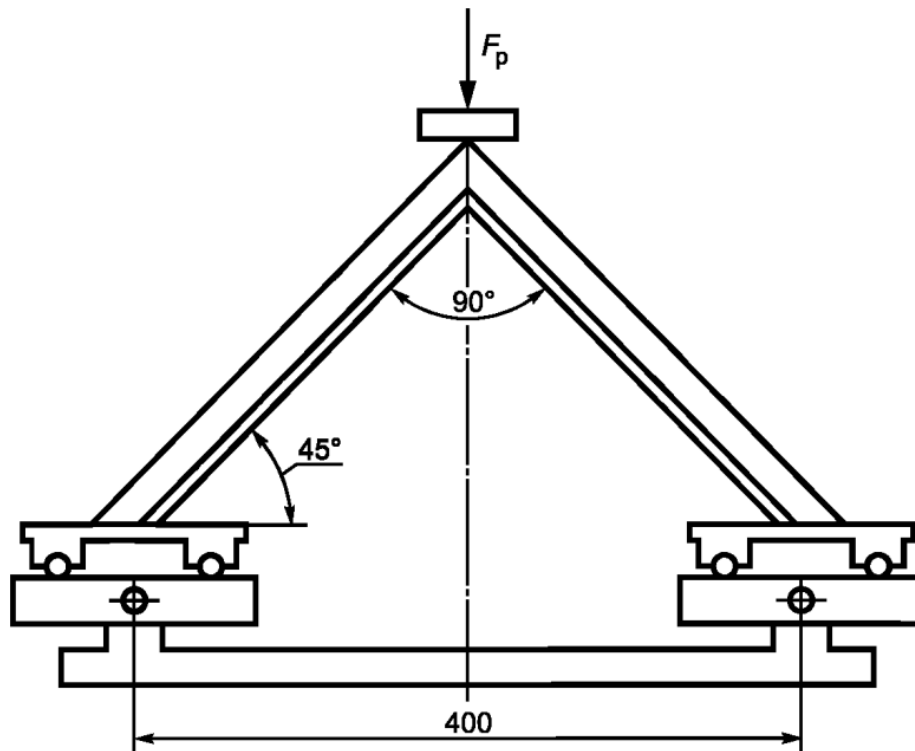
Схема испытаний для определения прочности угловых сварных соединений (определение разрушающей нагрузки F_p)
